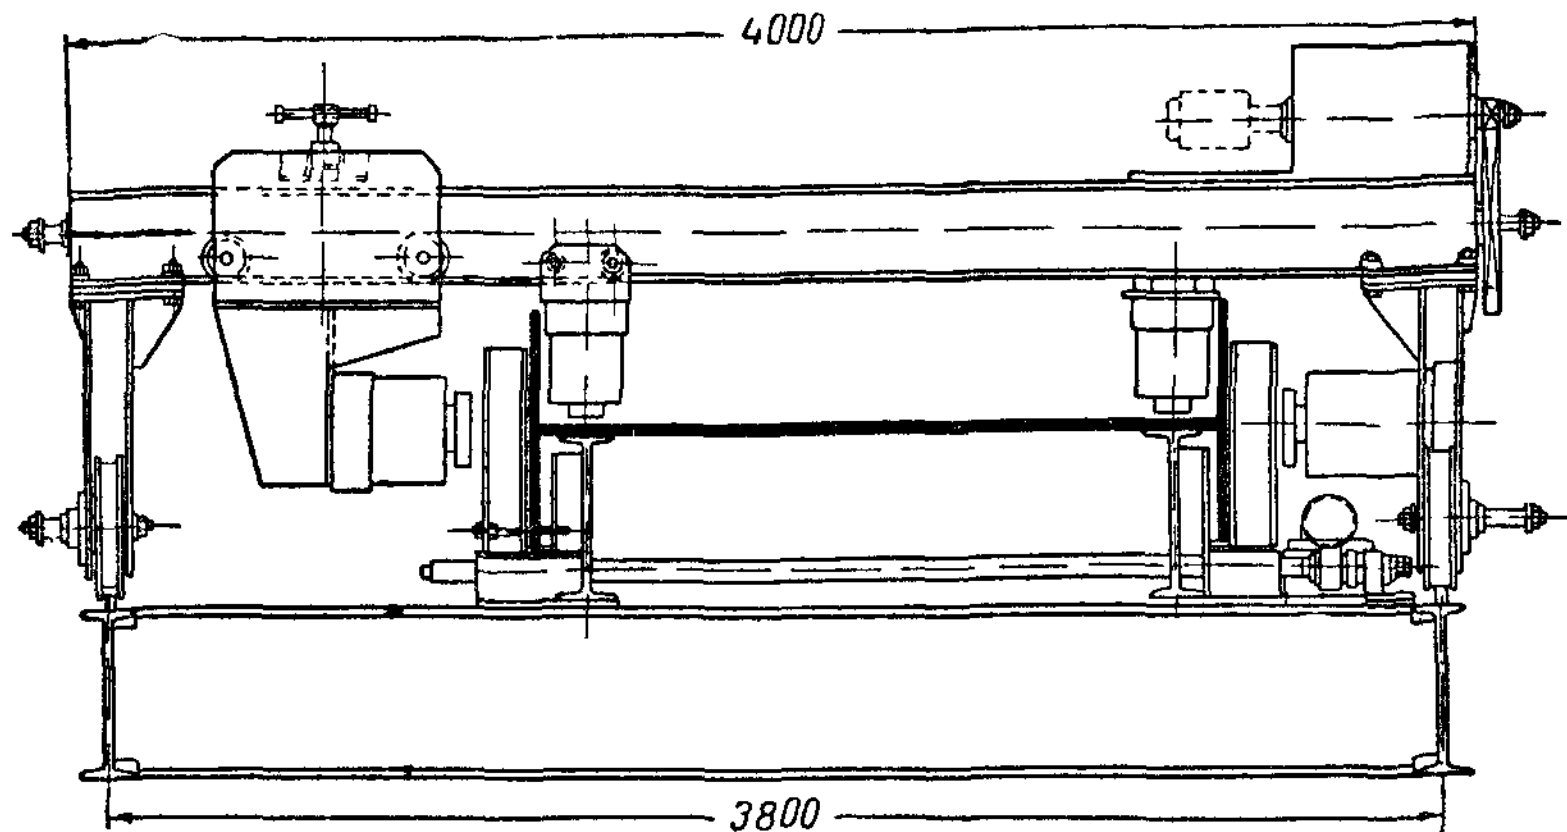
Механизированный кондуктор с передвижным порталом и пневматическими домкратами для сборки сплошных конструкций двутаврового сечения
